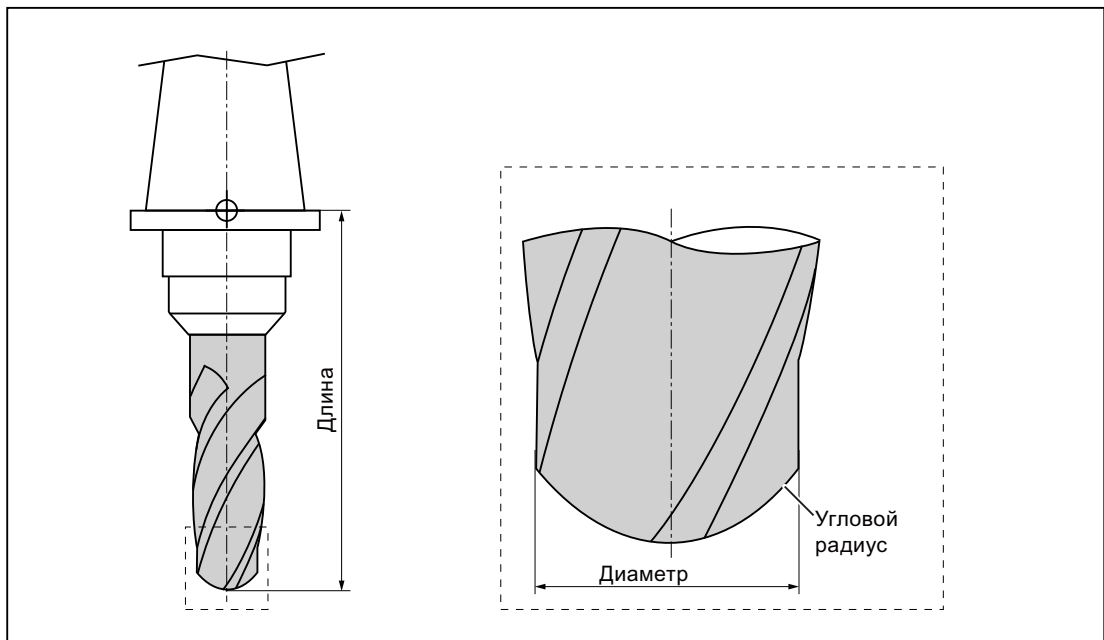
Тип инструмента 3D на примере сферической фрезы (тип 111)
